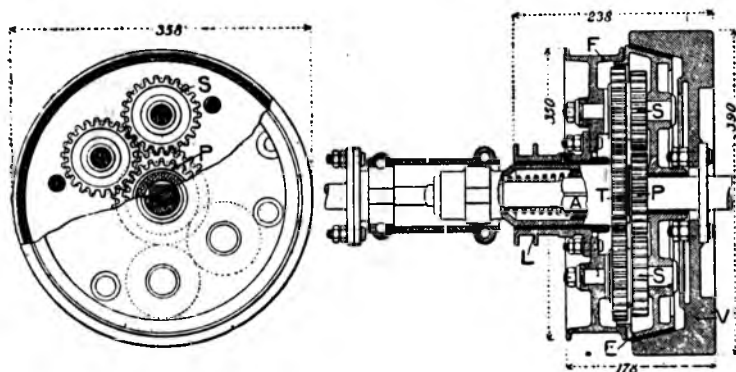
Механизм перемены вращения и разобщения двигателя от винта — с цилиндрическими зубчатками вместо конических. Механизм допускает уменьшение числа оборотов винта сравнительно с двигателем при обратном вращении. — *V* маховик двигателя. — *Е*, конус сцепления. — *P*, зубчатка насаженная на конце коленчатого вала двигателя. — *S*, зубчатка на промежуточной оси, вращающаяся лишь при заторможении барабана *F* и одновременном освобождении конуса *Е*. — *T*, зубчатка на конце гребного вала. — *A*, квадрат, допускающий отодвигание конуса посредством закраин втулки *L*. — Кроме обратного вращения, получается уменьшение числа оборотов винта при обратном ходе. (Сист. *Демаре-Моран*).
